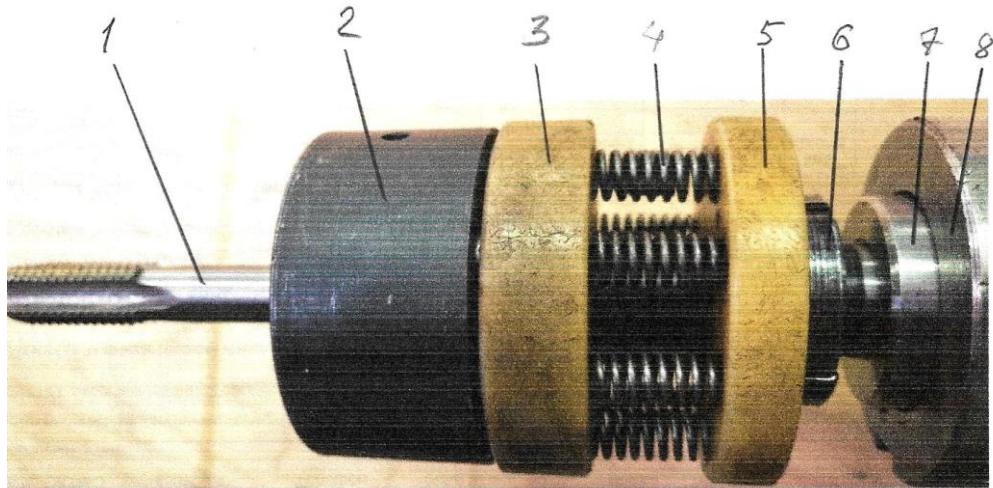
Пружинно-шариковый предохранительный патрон для метчиков, установленный на токарном станке: 1 – метчик; 2 - неврещающая шайба – мечикодержатель; 3 – вращающаяся шайба; 4 – пружины; 5 – нажимное кольцо; 6 – регулировочная гайка; 7 – хвостовик; 8 – пиноль задней бабки.
